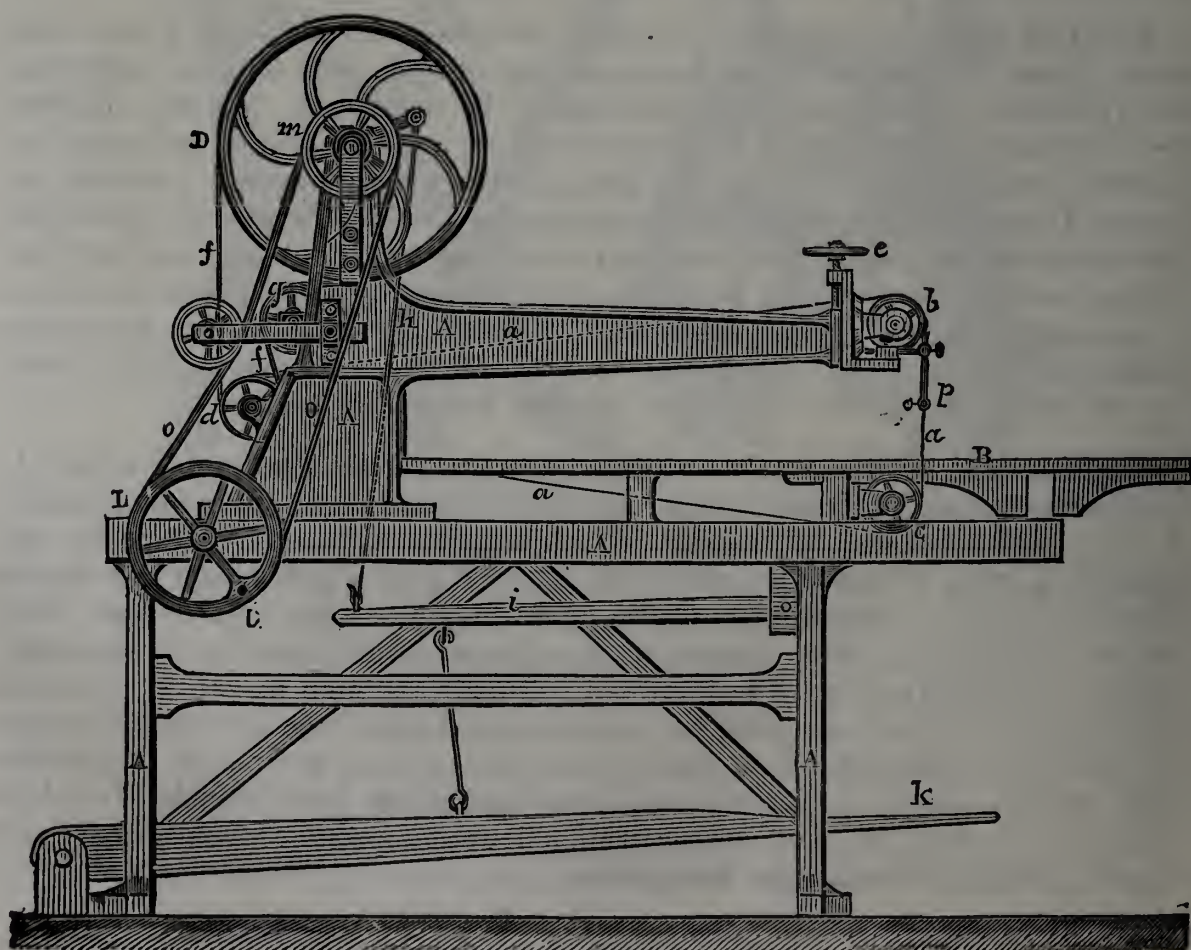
Machine à couper les tissus, de M. Langlois.
